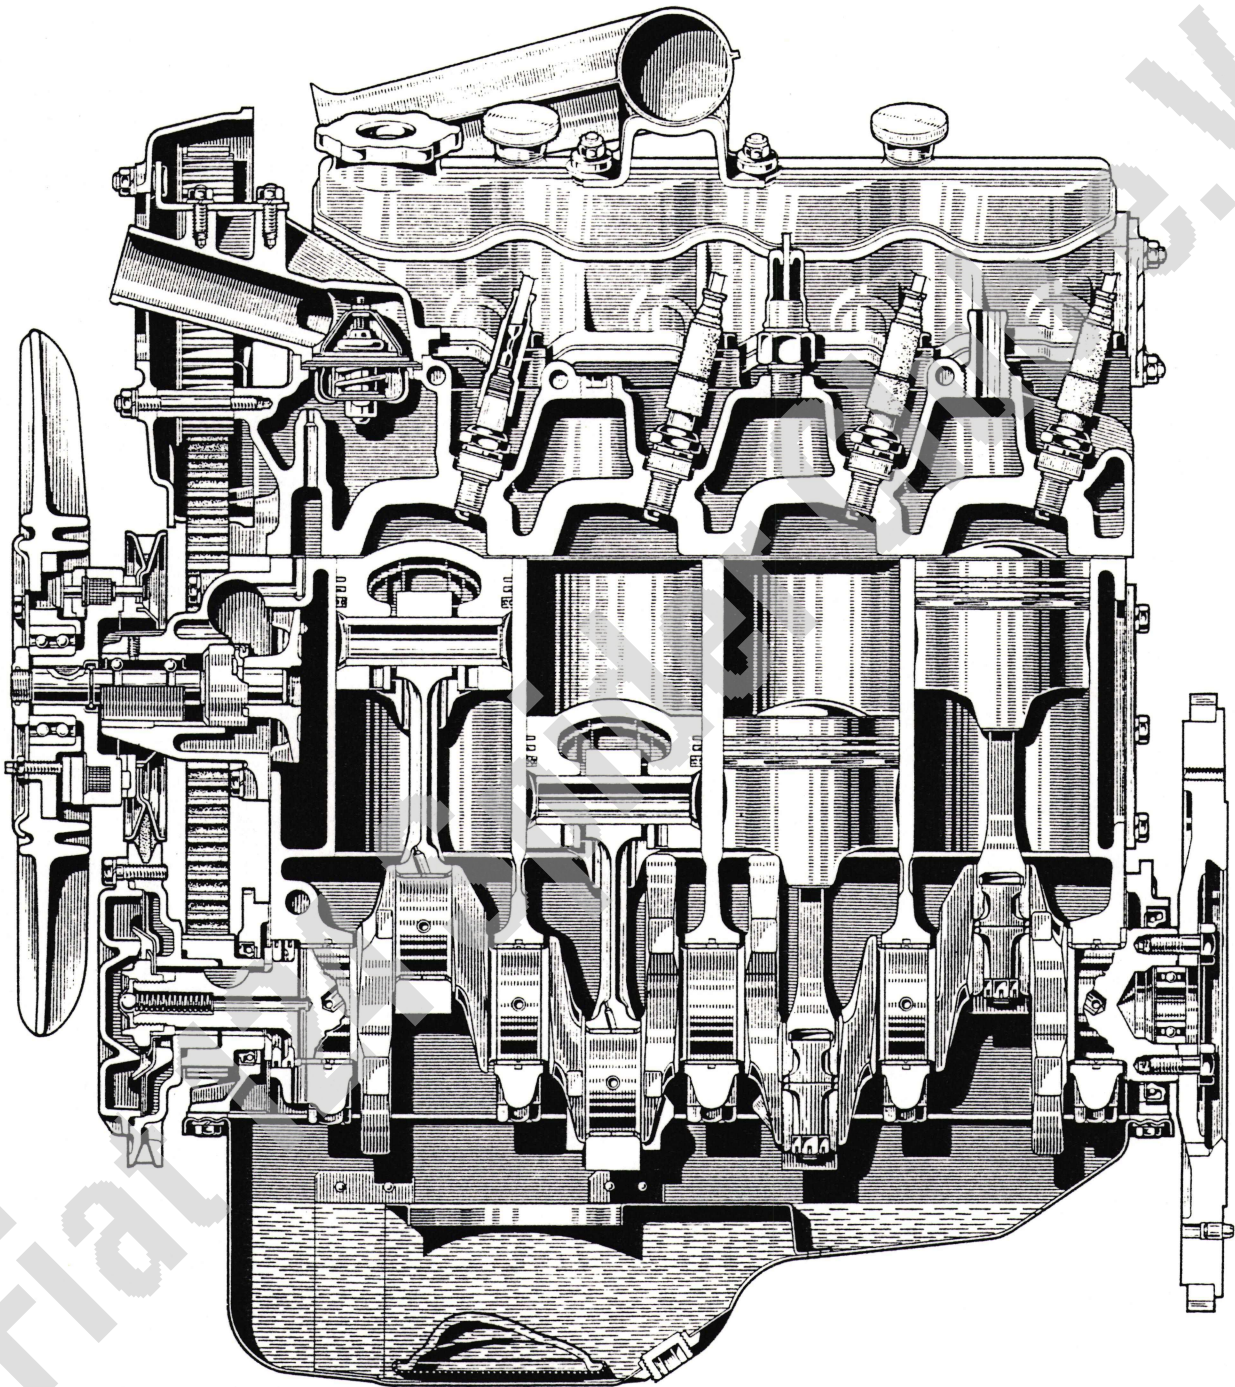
Längsschnitt durch die Zylinder des Motors.
